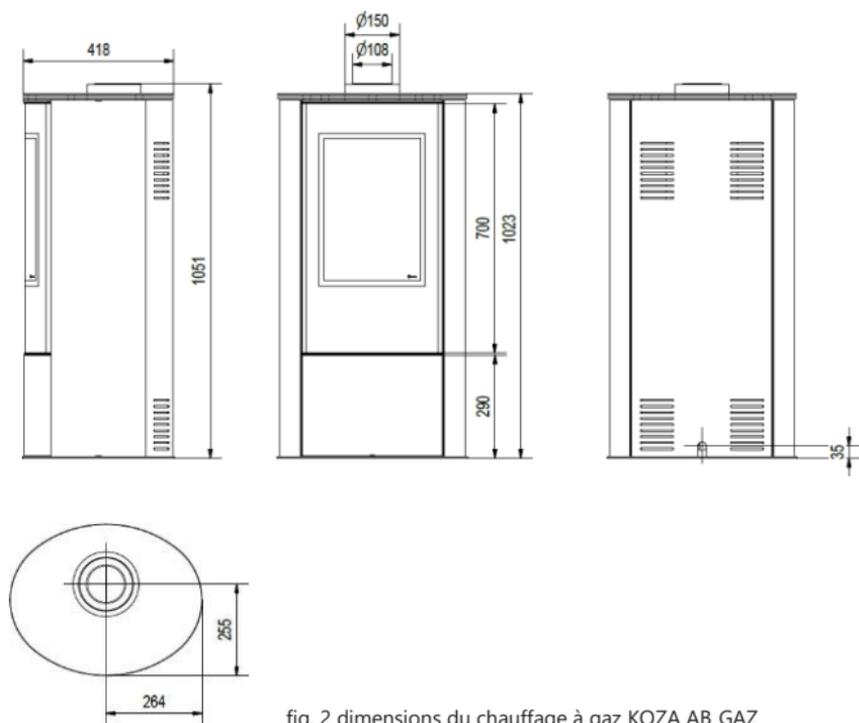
dimensions du chauffage à gaz KOZA AB GAZ
